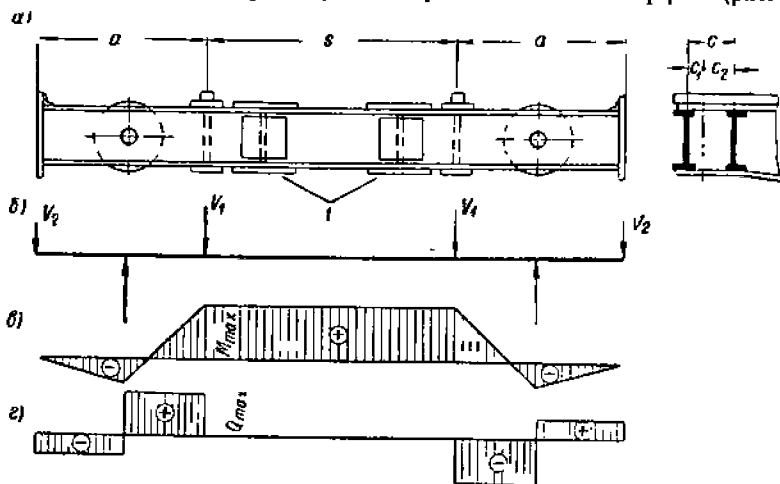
Концевая балка решетчатого моста: а — конструкция балки; б — схема нагрузок; в — эпюра M ; г — эпюра Q ; 1 — монтажные болтовые (заклепочные) стыки
